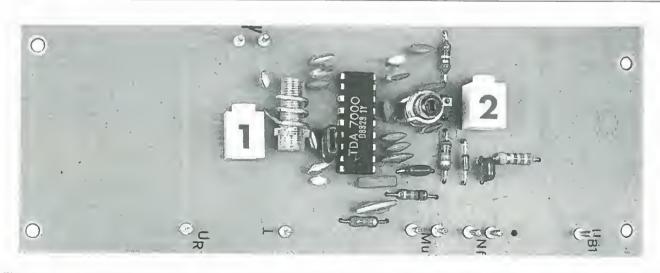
La basetta del ricevitore FM dovrà avere piccole dimensioni, con un montaggio molto raccolto dei componenti: le dimensioni sono 52 x 135 mm.
